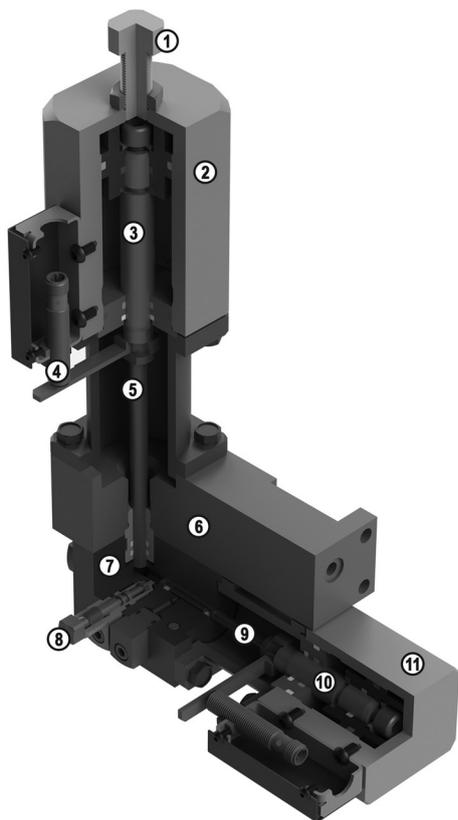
Смесительное устройство высокого давления: 1 – винт регулировочный; 2 – цилиндр вертикальный; 3, 5, 9 и 10 – шток; 4 – датчик конечного положения; 6 – пластина; 7 – корпус; 8 – игла; 11 – цилиндр горизонтальный
